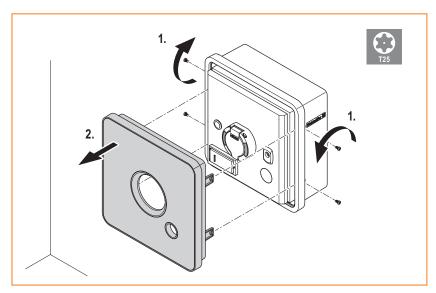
Gehäusedeckel vom Gehäuse abschrauben
